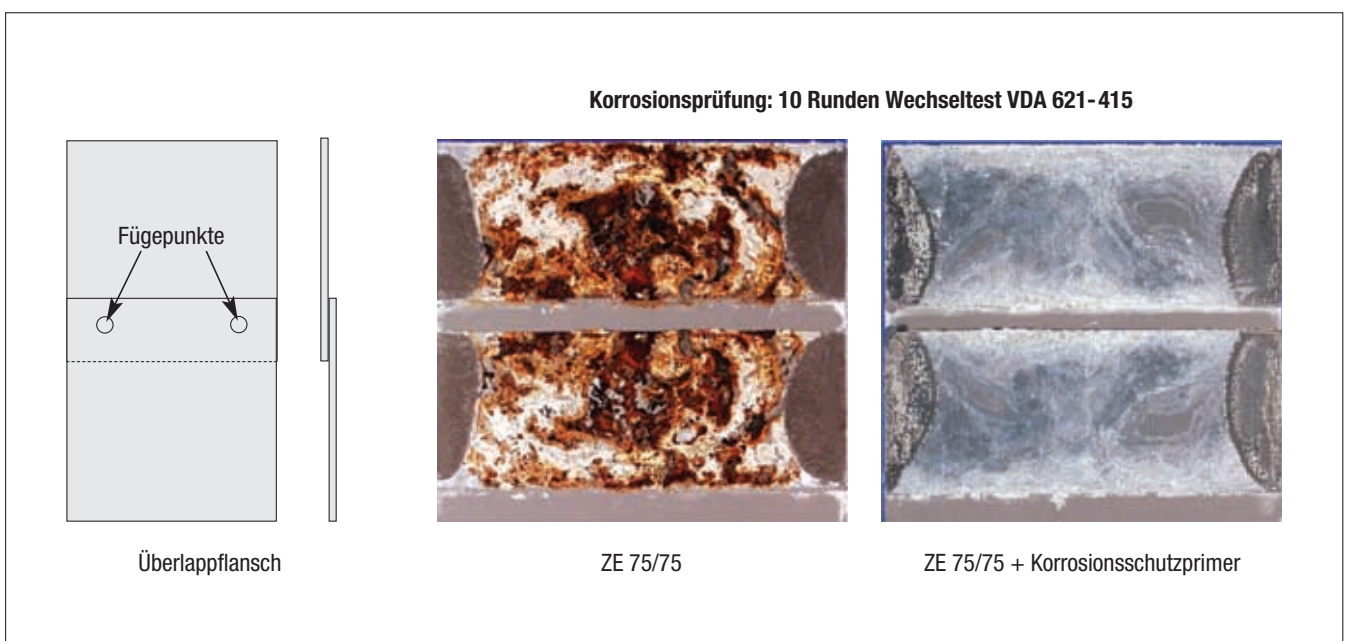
Korrosionsverhalten von Karosserieblech mit Korrosionsschutzprimer im Modellflansch (geöffneter Flansch)
